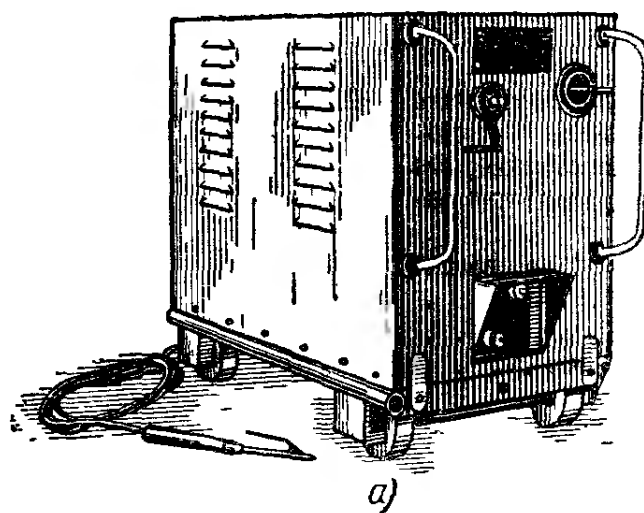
Сварочный селеновый выпрямитель ВСС-120
